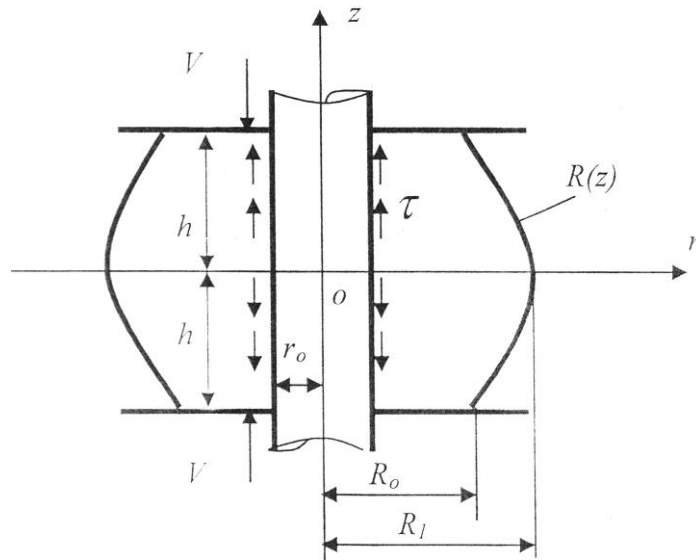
Схема осадки полой цилиндрической заготовки с оправкой
